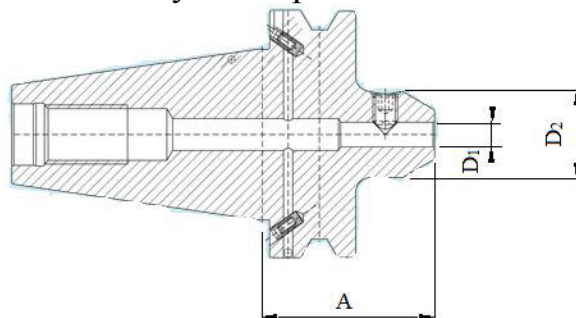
Патрон Weldon 50.500.25 для сверла:
